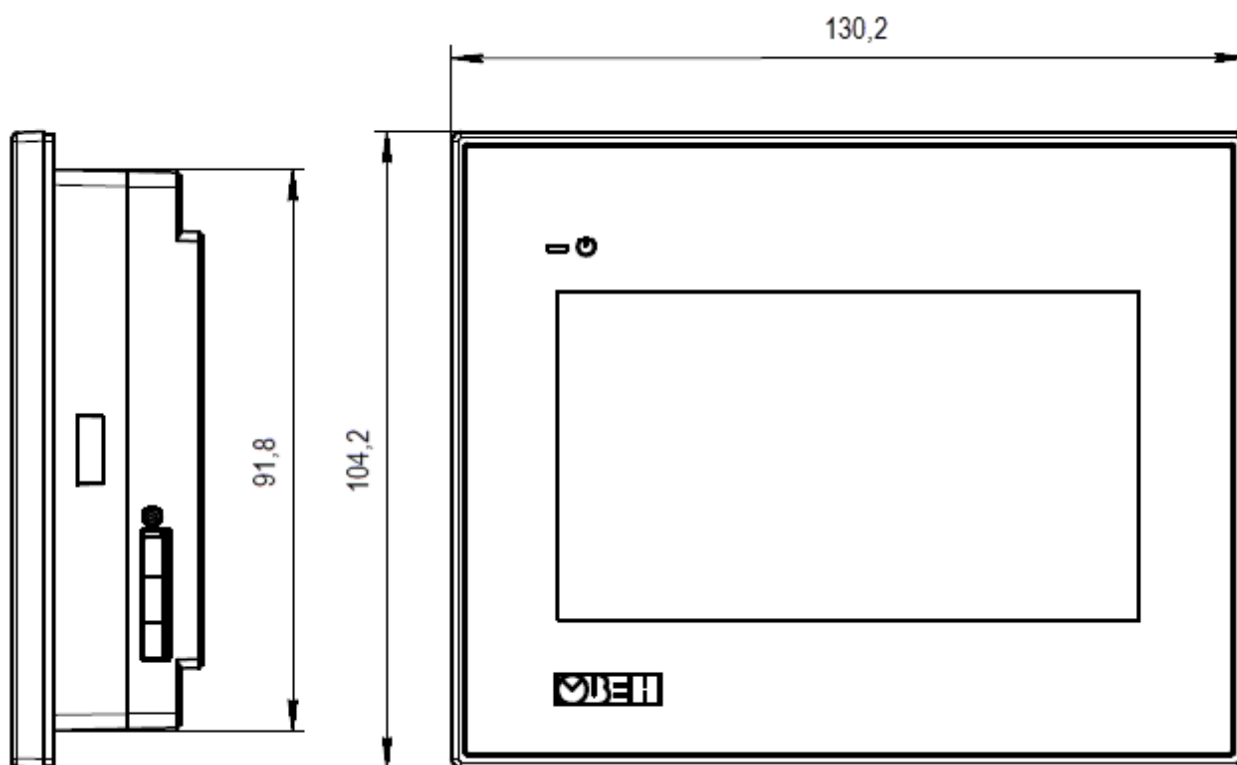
Габаритные размеры СП210-05-Б и СП210-05-Р
